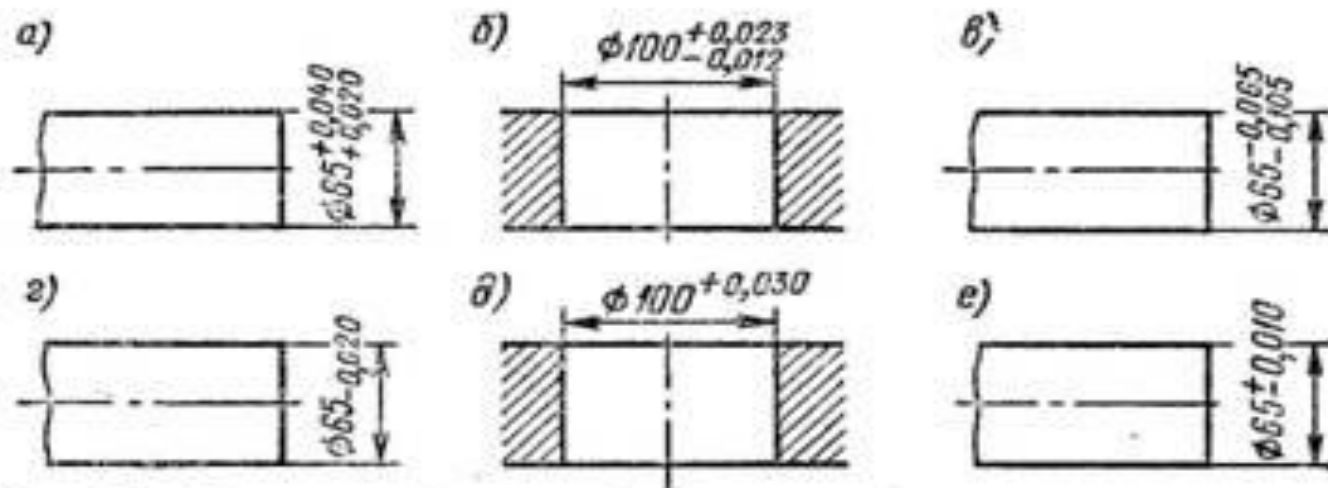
Примеры обозначений на чертежах допусков числовыми значениями отклонений
